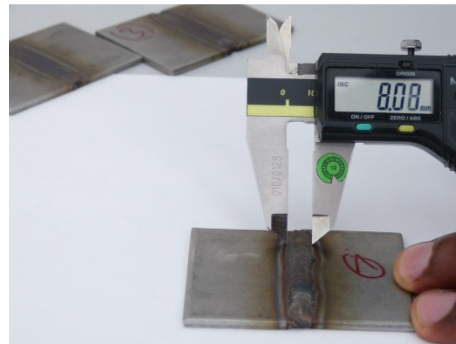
Tôles soudées avec soudure complète dans la profondeur - - Mesure de la largeur du cordon
